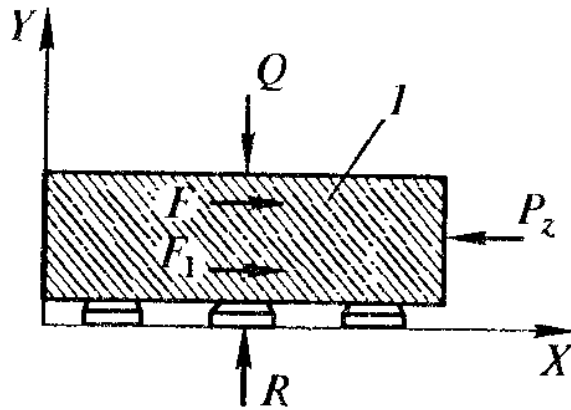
Напрямок сил різання P_z і затиску Q при установці заготовки в пристосуванні
